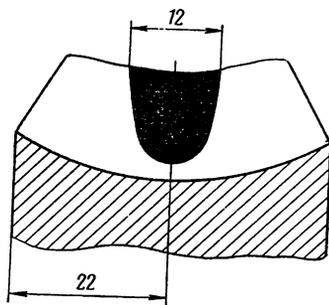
Положение пятна контакта на зубьях ведомой шестерни
